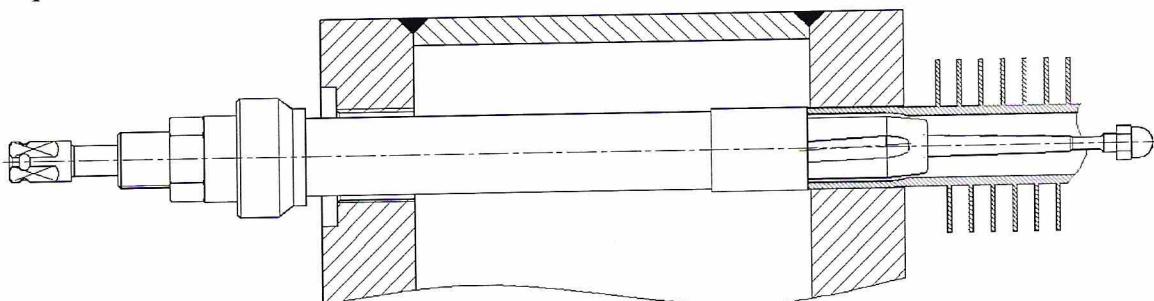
Вальцовка с удлиненной обоймой в сварной камере
